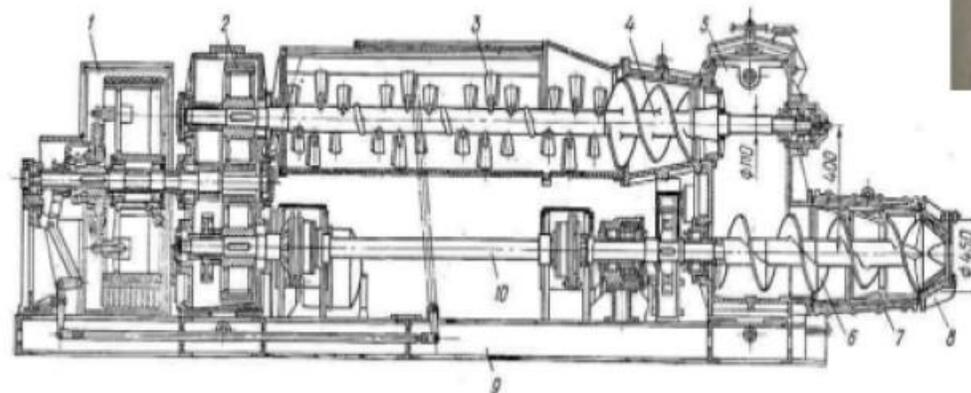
Ленточный вакуумный комбинированный пресс СМК-28 (СМ-443А):
